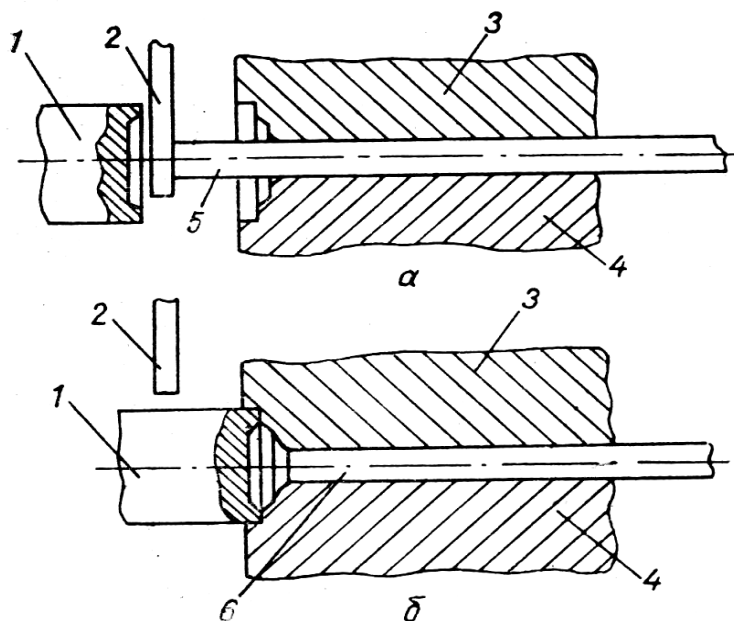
Стадії виготовлення (а, б) заготовок клапанів на ГKM: 1 — пуансон; 2 — упор; 3, 4 — частини рознімної матриці; 5 — вихідна заготовка; 6 — кованка
